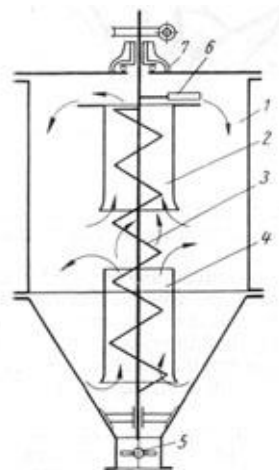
1 – бункер, 2 – верхний патрубок, 3 – вертикальный шнек, 4 – нижний патрубок, 5 – разгрузочный клапан, 6 – сбрасывающая лопасть, 7 – привод
